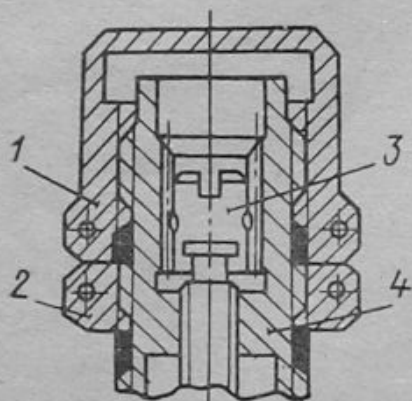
Регулировочные винты № 7 и № 9 агрегата АТП в сборе:
